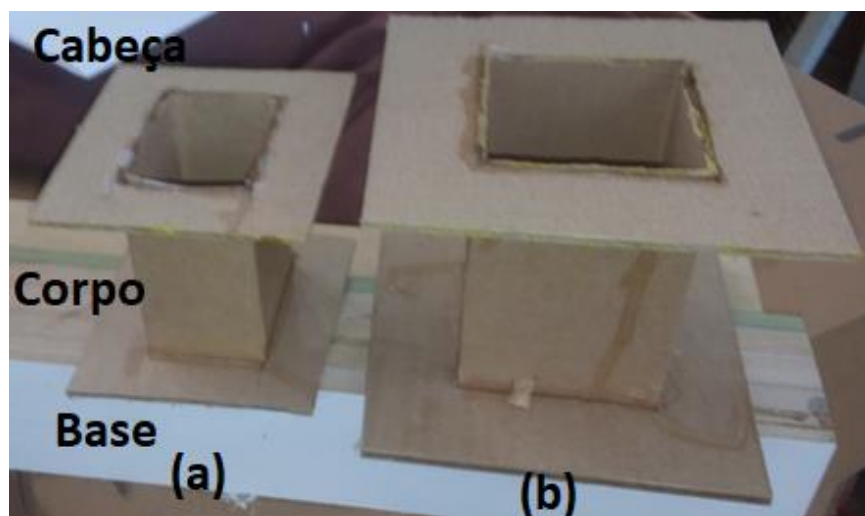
Carretéis produzidos artesanalmente: (a) para transformador com enrolamentos de cobre; (b) para transformador com enrolamentos de alumínio.
